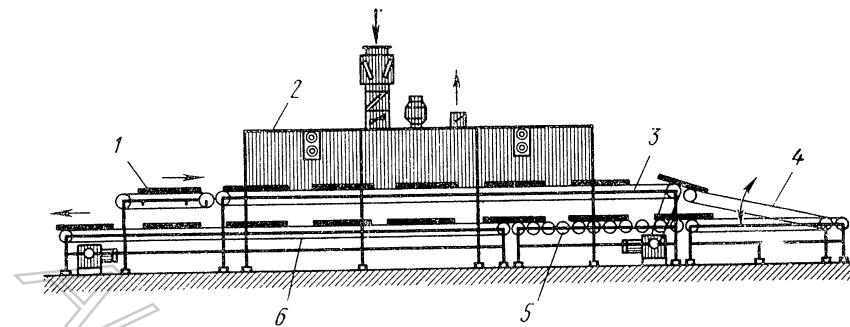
Схема проходной камеры с расположением деталей на конвейере:
